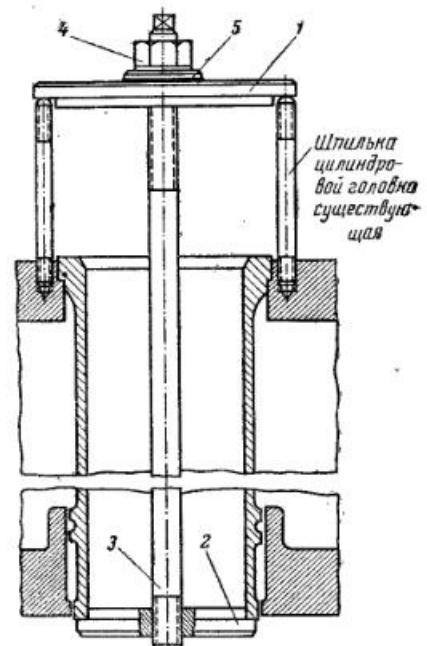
Приспособление для выпрессовки цилиндровой втулки двигателей типа NVD-24:
